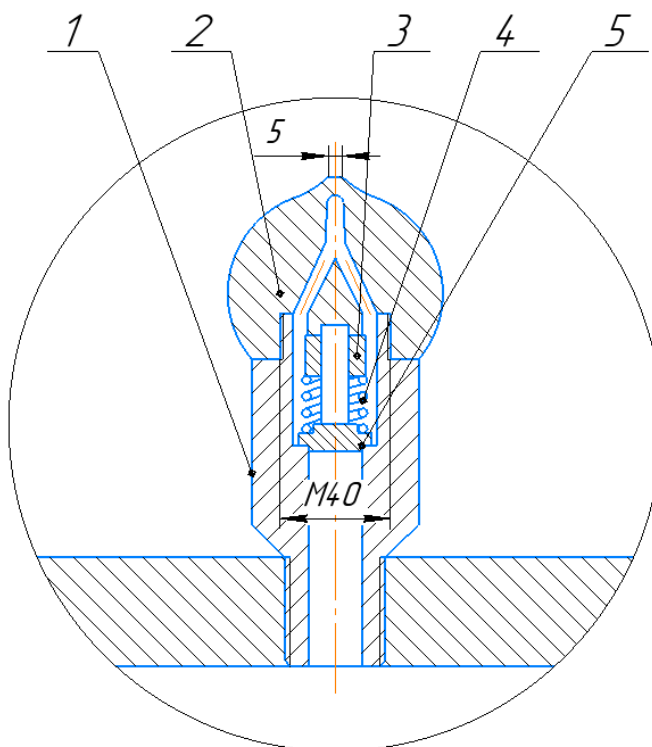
Форсунка: 1 – корпус форсунки; 2 – основание сопла;
